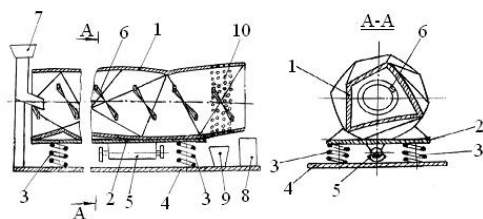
Роторно-винтовой станок с виброконтэйнером с пружиной растяжения
